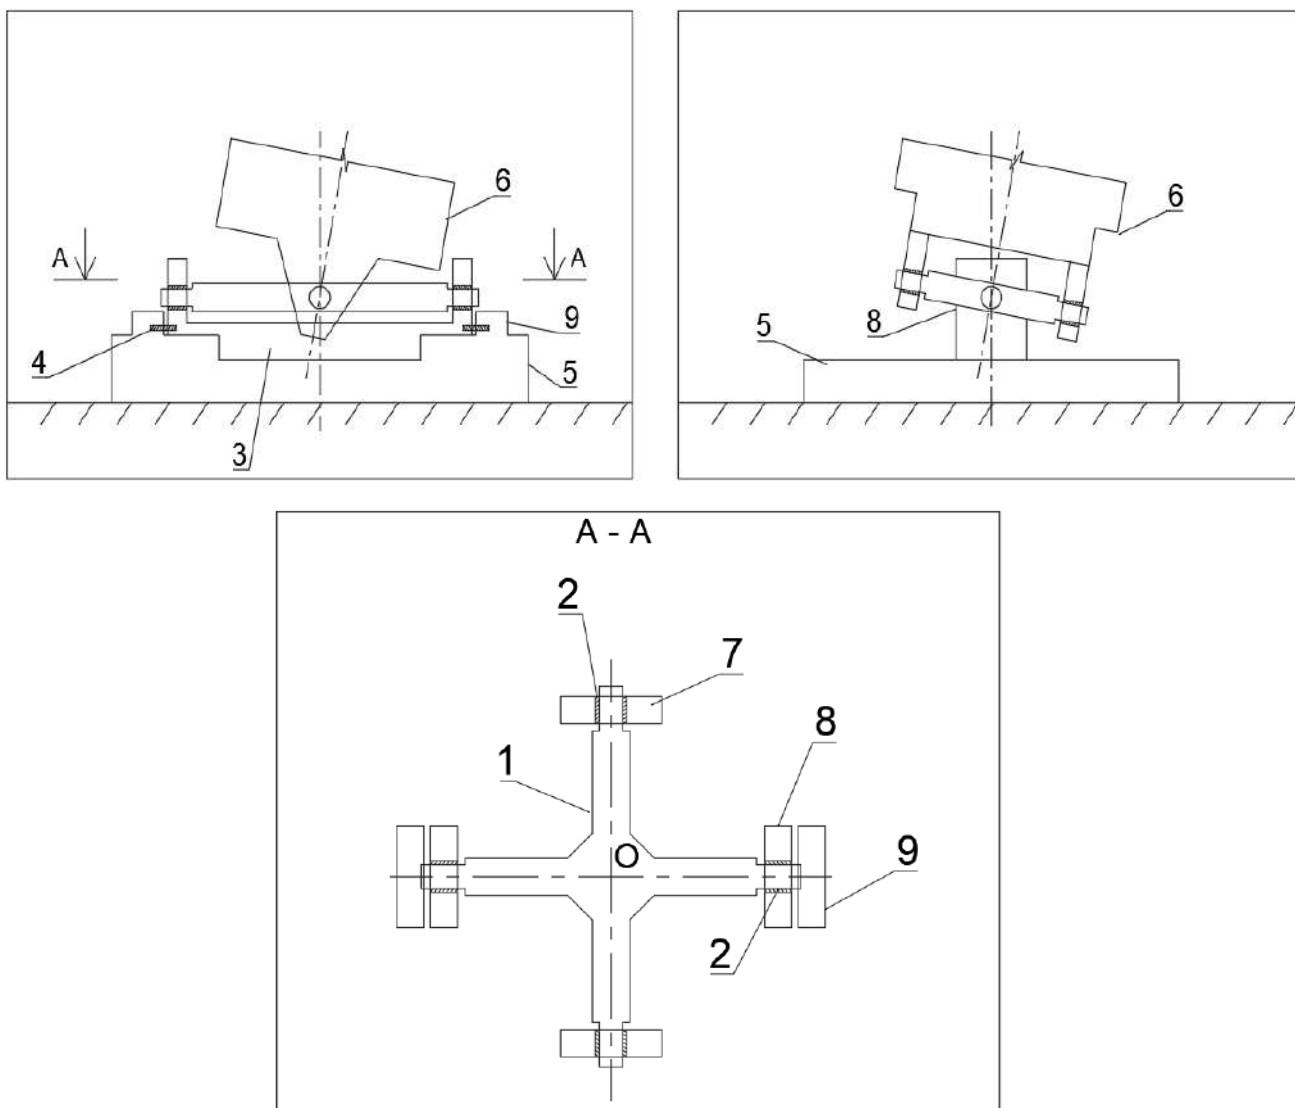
Схема карданного шарнира: 1 – крестовина кардана; 2 – подшипники; 3 – соединительная плита; 4 – гидравлический замок; 5 – основание; 6 – опора; 7 – стойка подшипника опоры; 8 – стойка подшипника соединительной плиты; 9 – упор основания; О – центр кардана
